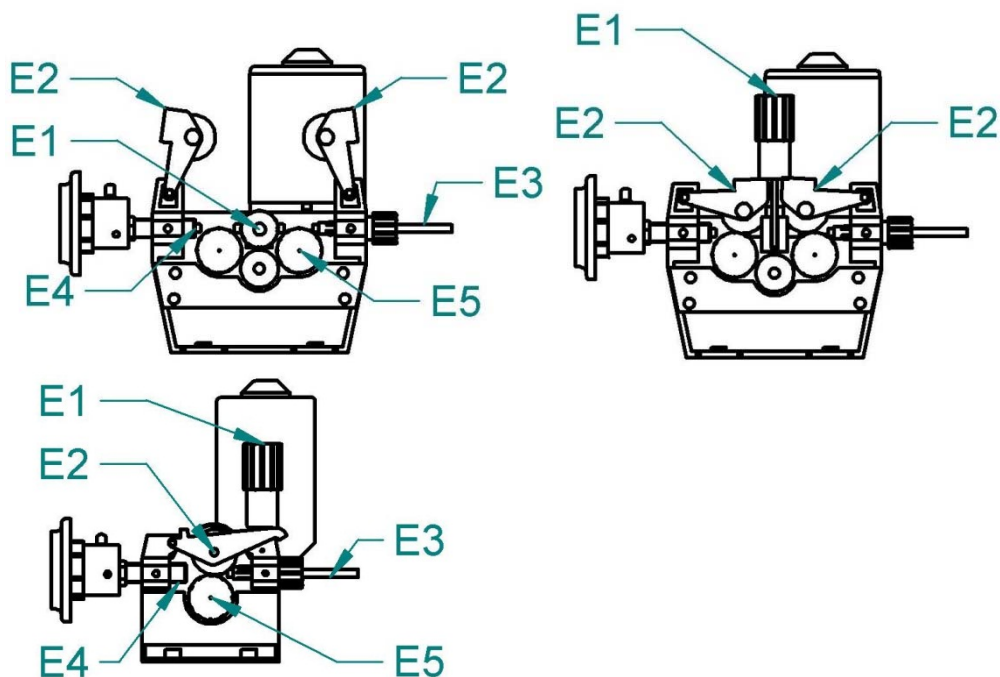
Drahtvorschub 4–Rollen, 2-Rollen
